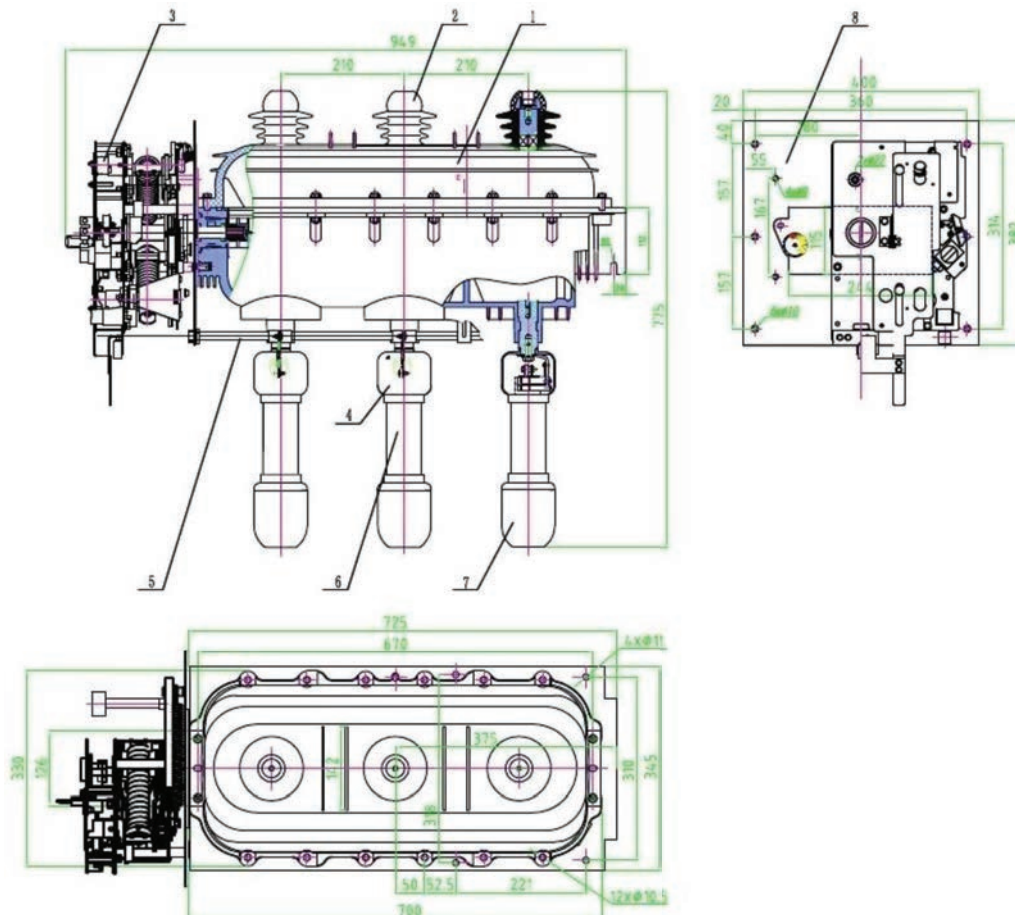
Размеры выключателя нагрузки с предохранителями
